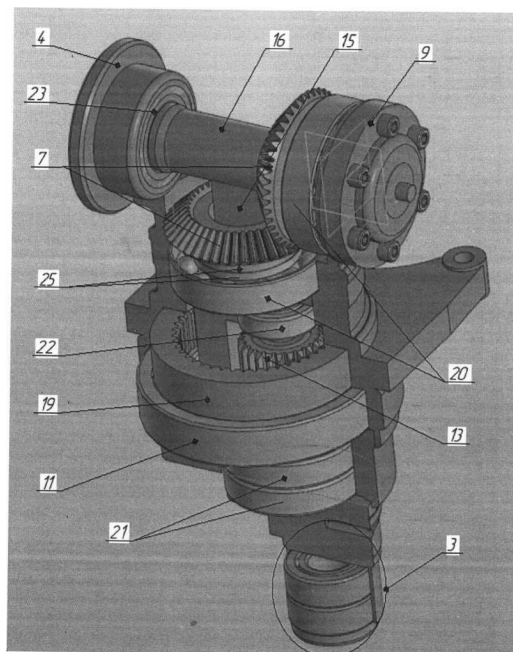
3D-модель зубчато-эксцентрикового механизма
